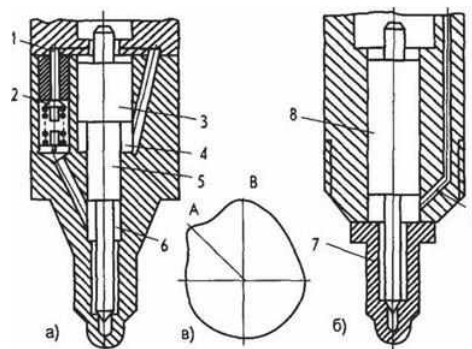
Довгокорпусні розпилювачі: а – з двухдиференціальною голкою; б – з окремим соплом; в – профіль кулачка паливного насоса, що працює на форсунку; 1 – канал підведення палива; 2 – зворотний клапан; 3,5 – прецизійні поверхні; 4, 6 – порожнини; 7 – сопло; 8 – голка; 9 – канал
